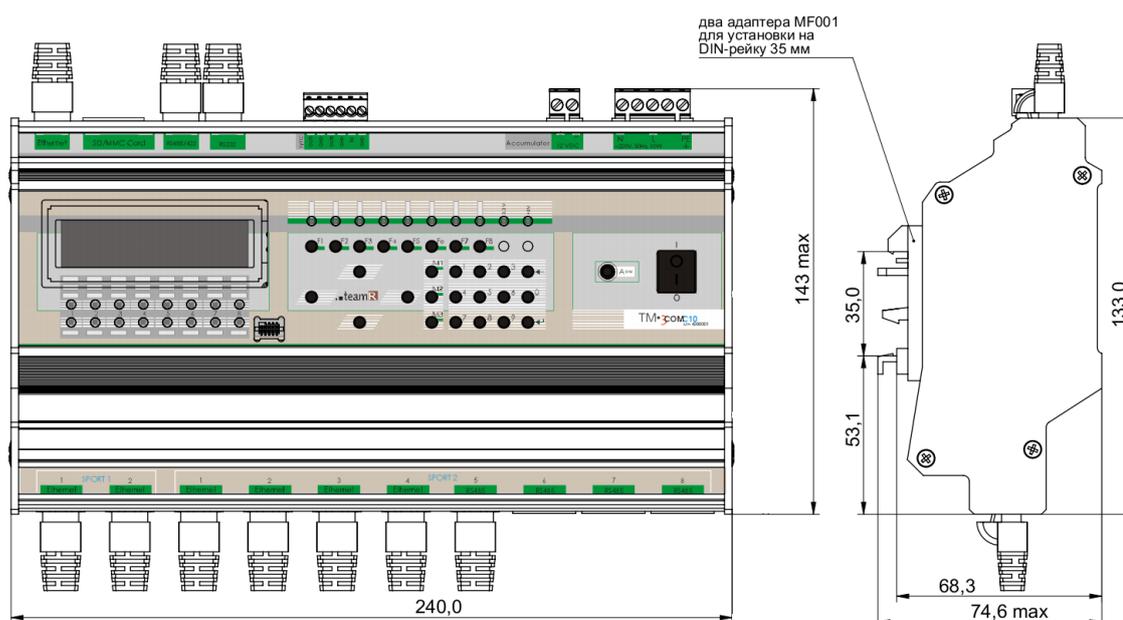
Габаритный чертеж УТМ ПУ «ТМ3com»
